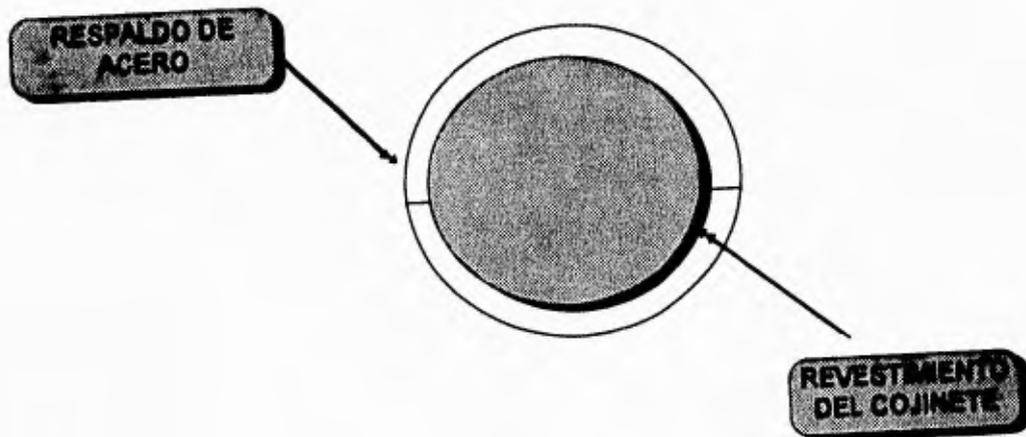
VISTA FRONTAL DE UN COJINETE
